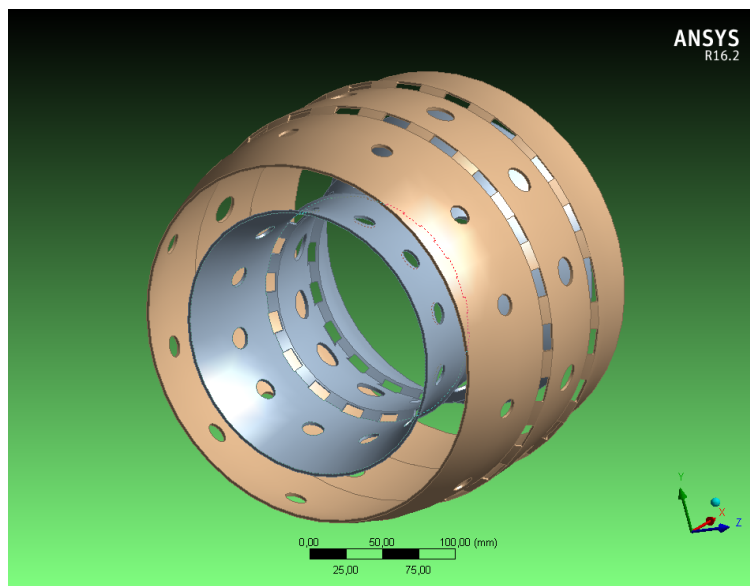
Внутренний и наружный корпус жаровой трубы готовой модели КС
